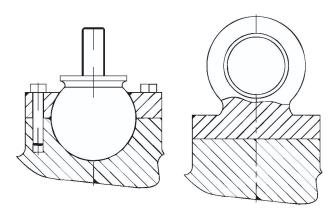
Die Varianten der beweglichen Befestigung der Stößdampfer der Aufhangung zum Rahmen und der Brucke des Kippers
